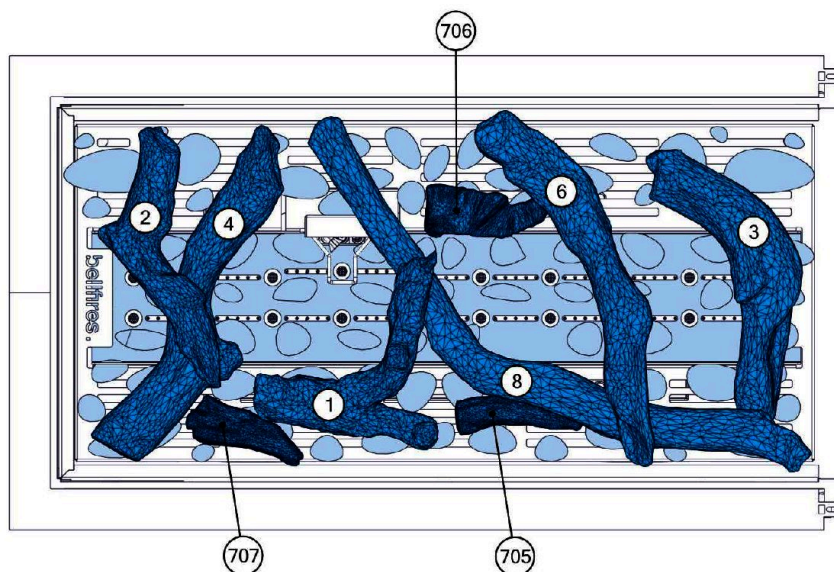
Lageschema Holzstammset Erdgasbrenner
